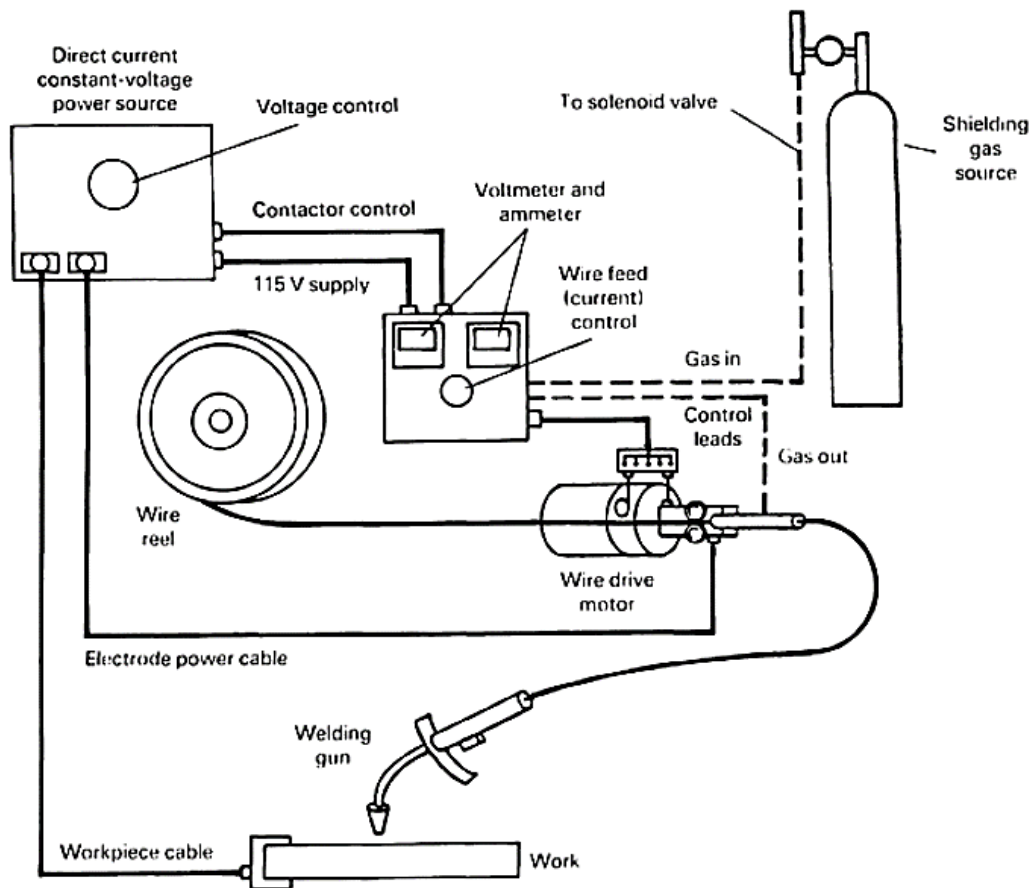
Partes del equipo de Soldadura FCAW
